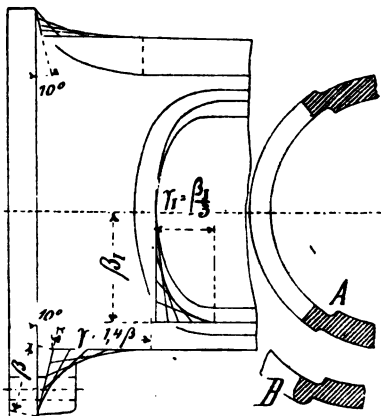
zeigt ferner den Anschluss der Rundführung an den Flansch mittelst Parabel.
